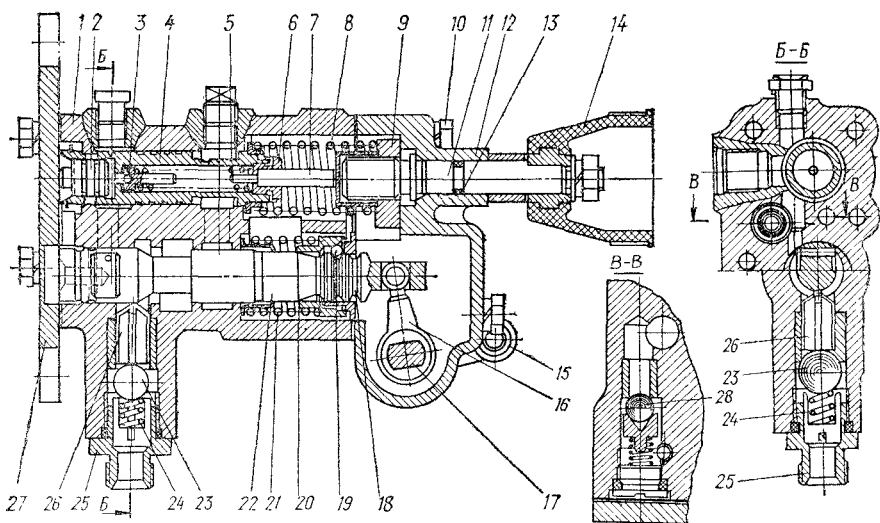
Конструкция гидроувеличителя сцепного веса:
